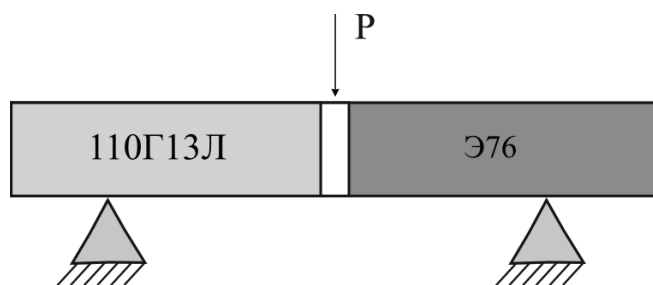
Схема испытания комбинированной сварной конструкции методом трехточечного изгиба
